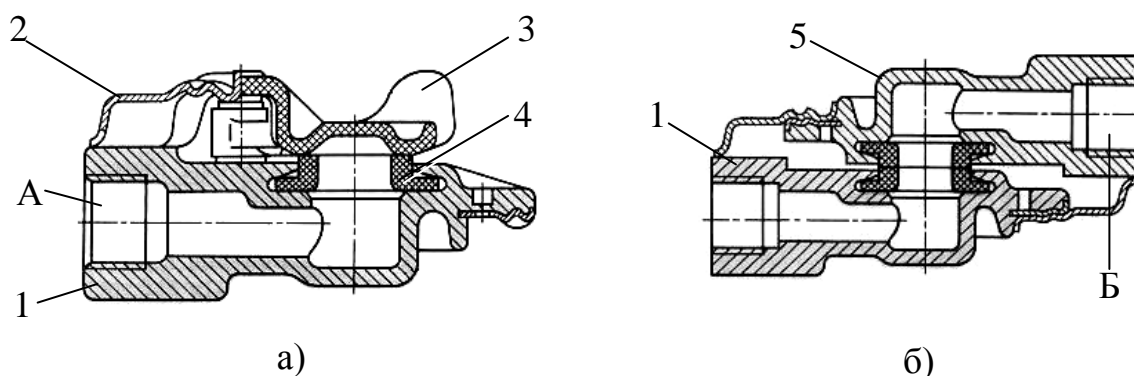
Конструкция узла соединения пневмосистем грузового автомобиля-тягача КАМАЗ и прицепа, связанных по двухпроводной схеме: а – соединительная головка типа «Палм», б – соединение головок тягача и прицепа; 1 – корпус головки тягача; 2 – фиксатор; 3 – крышка; 4 – уплотнение; 5 – головка прицепа; А – вывод в пневмосистему тягача; Б – вывод в пневмосистему прицепа
